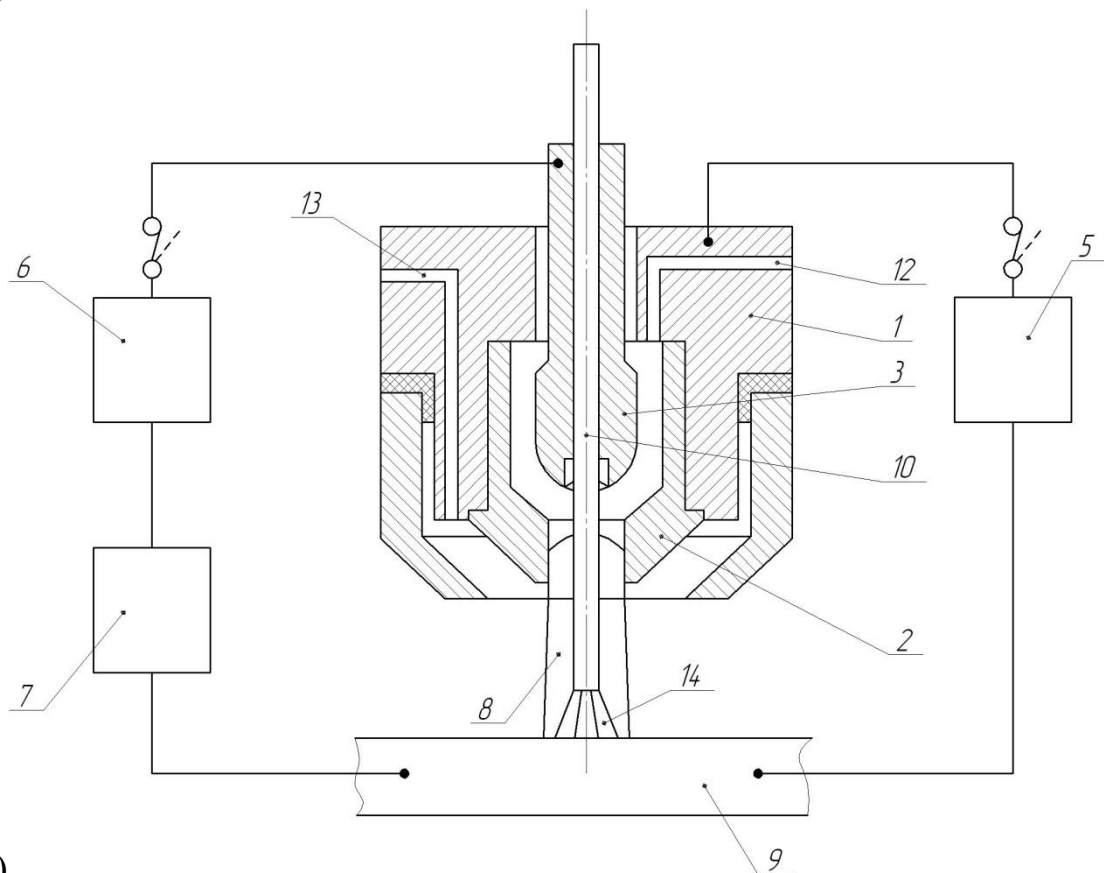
Схема выполнения гибридной сварки
